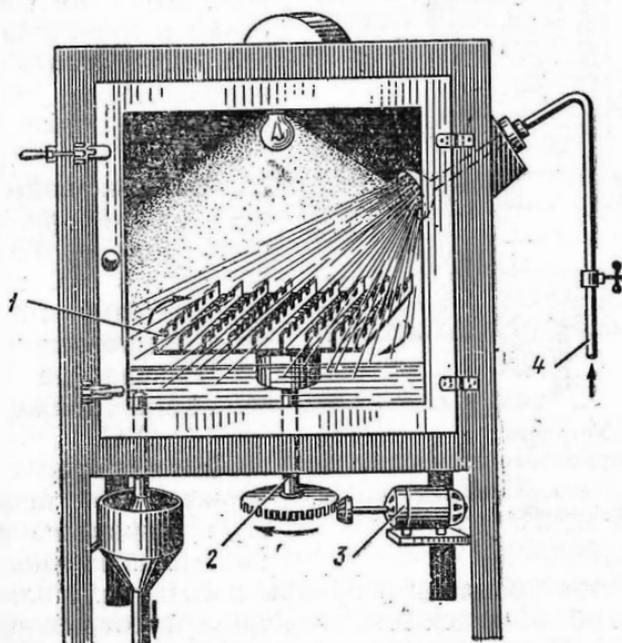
Камера для проверки часов с водозащитными корпусами:
